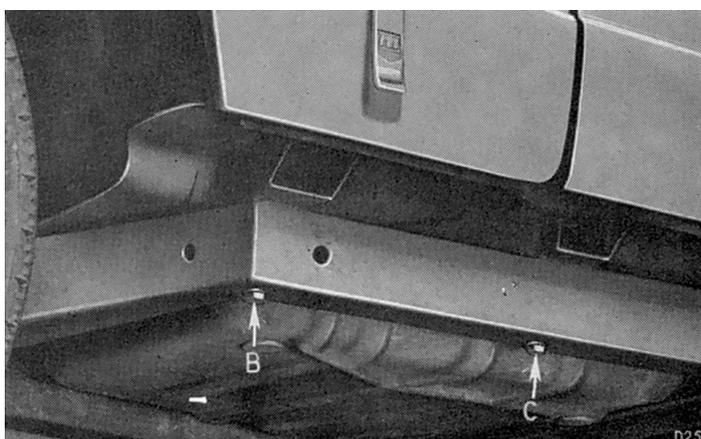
Fixation de la section centrale aux longerons latéraux du châssis
